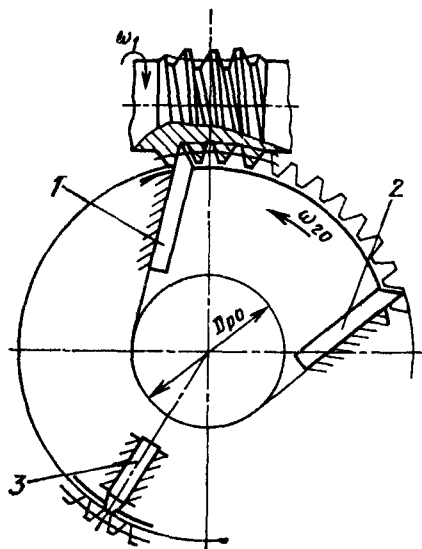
Схема трехрезцовой головки для нарезания витков глобоидного червяка:
